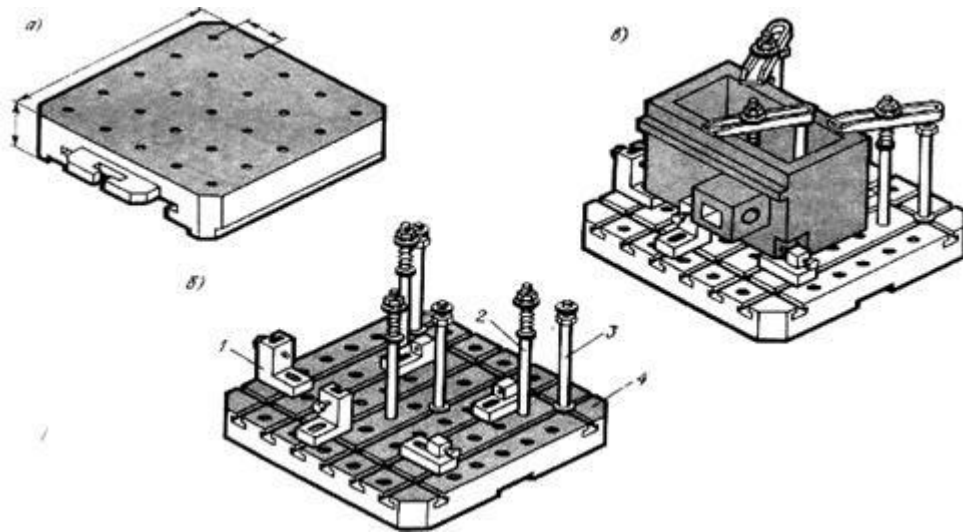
Пристосування-супутник; а - плита пристосування-супутника верстата IP 500МФ4; би - плита із закріпленням на ній пристосування; а - пристосування в зібраному виді зі встановленою деталлю.
